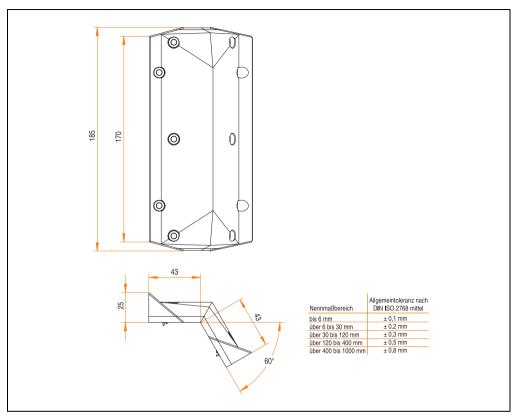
Abmessungen Extension Connector 60° 5AC800.CON2-00
